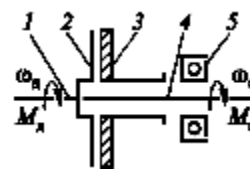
Принципова схема механічного фрикційного зчеплення: 1, 4 – ведучий і ведений вали; 2, 3 – ведучий і ведений диски; 5 – натискний підшипник
